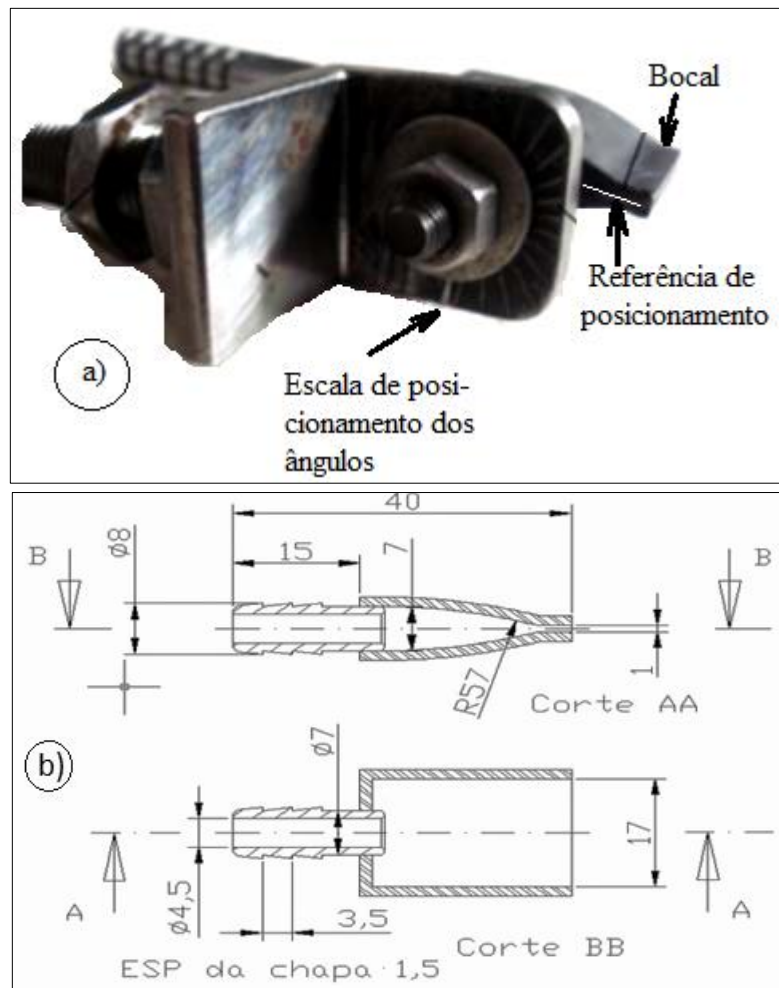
Bocal de Limpeza – a) Posicionador, b) Desenho técnico.
